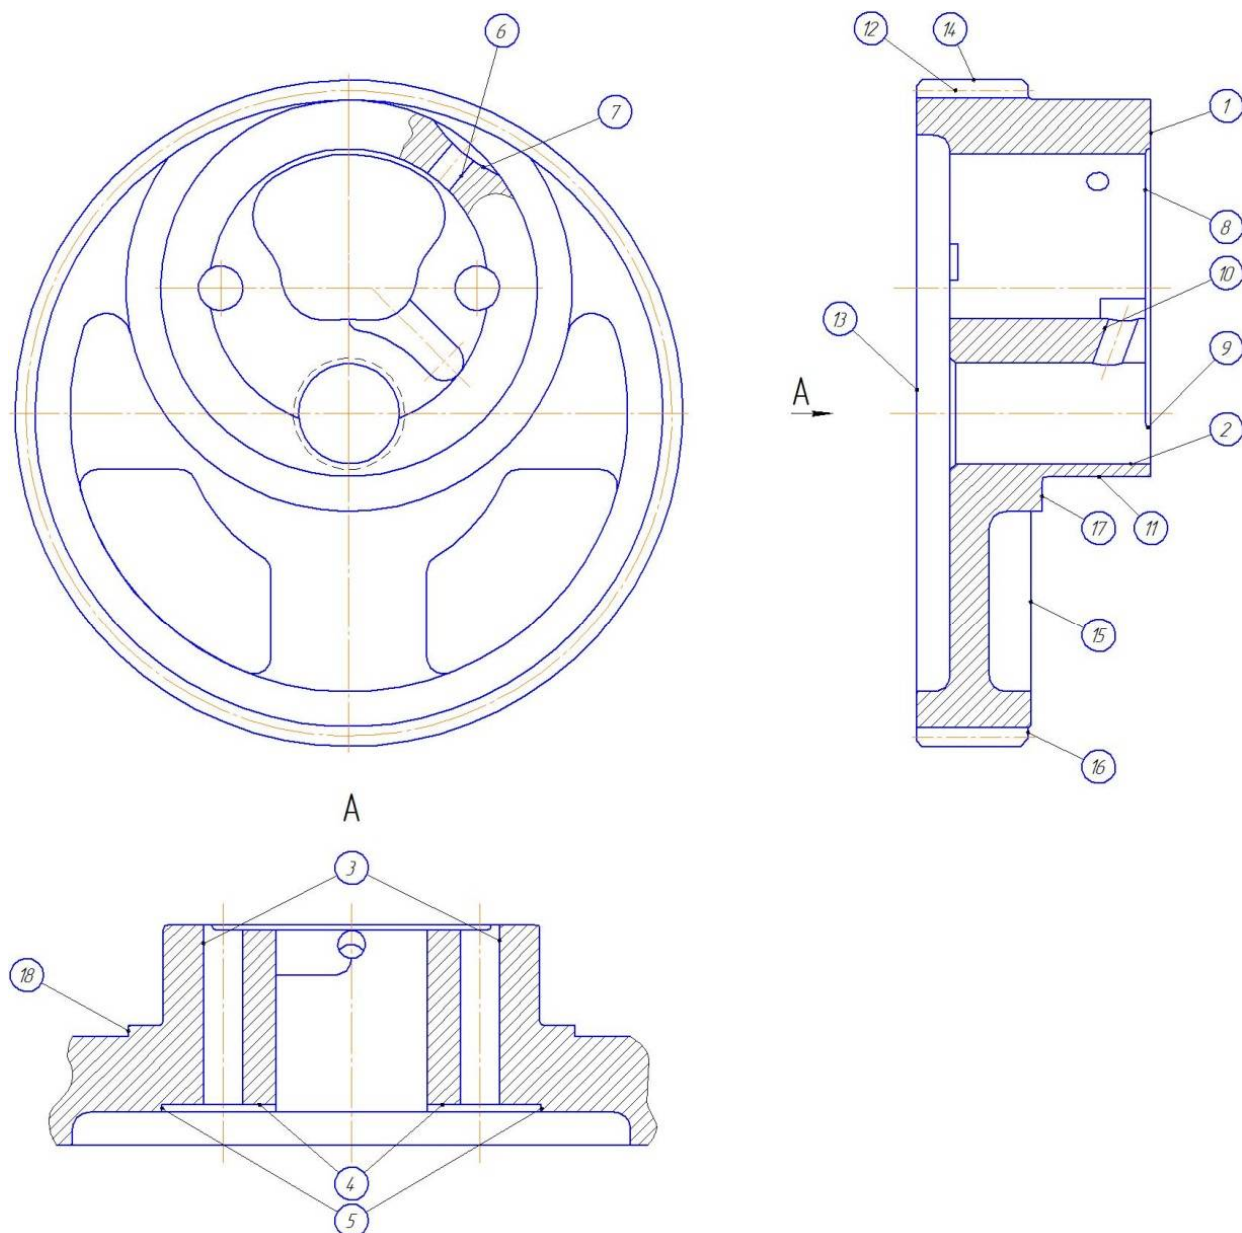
Ескіз деталі «Шестерня ШВП 72.01»
